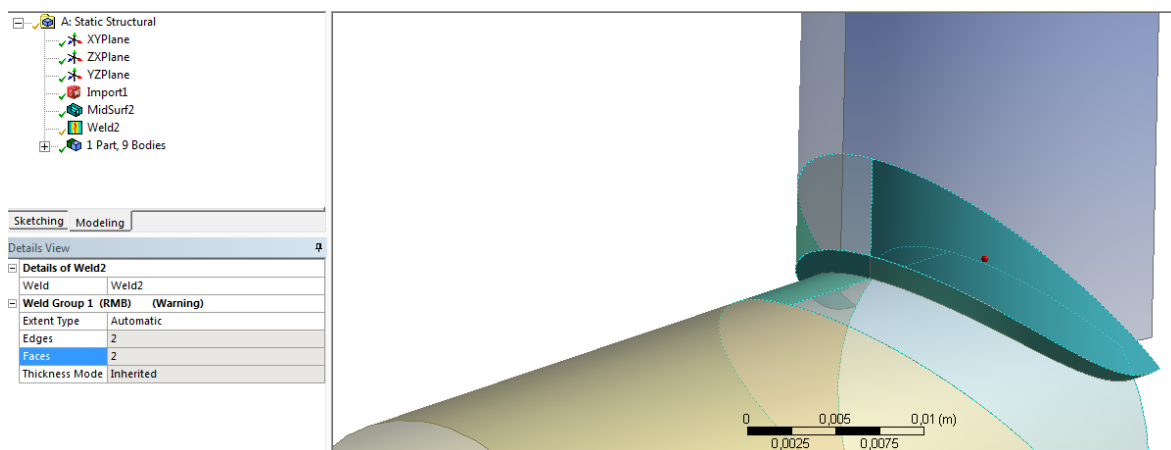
Ferramenta *Weld Tool
